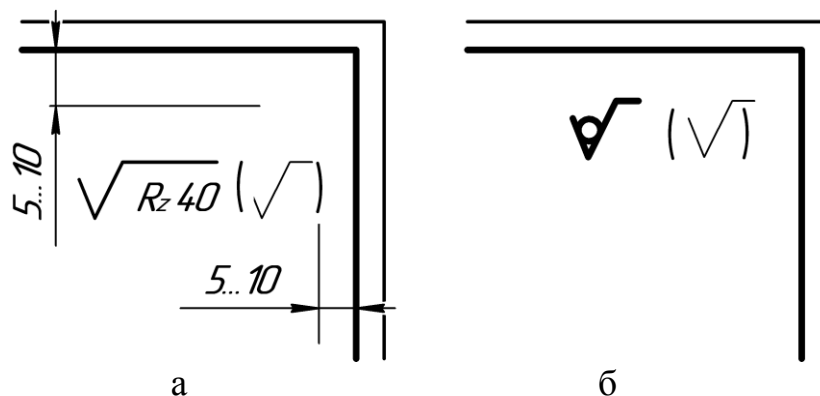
Обозначение преобладающей шероховатости поверхностей на рабочем чертеже
